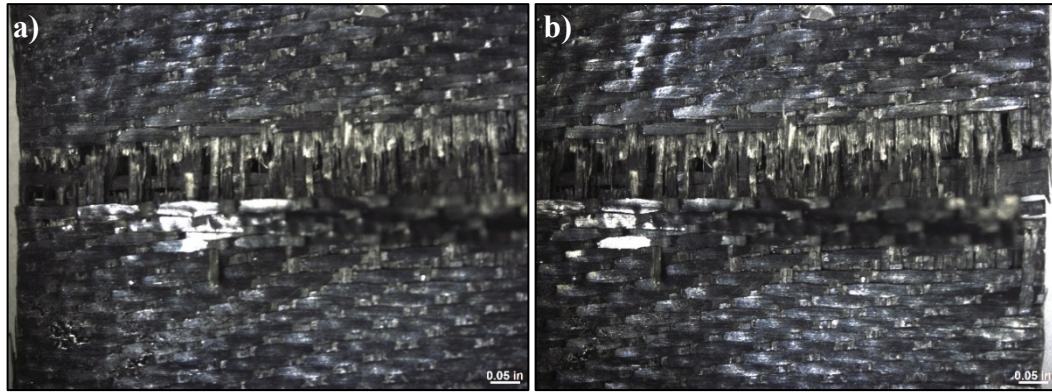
Inspección visual de probeta 2 de 3 capas a la falla, que presenta un código de falla AGM a) extremo izquierdo y b) extremo derecho de la probeta con fractura expuesta.
